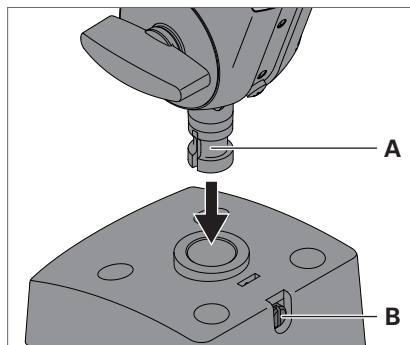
Montare l'apparecchio di illuminazione sull'elemento di fissaggio.
